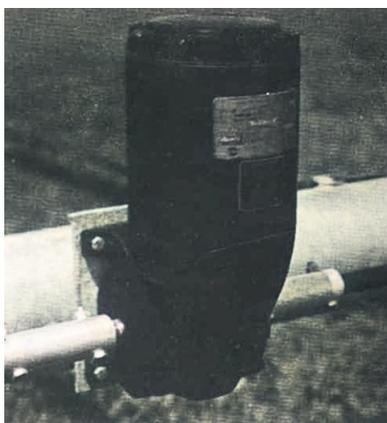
Центральный мотор-редуктор ДМ с передачей червячного типа
